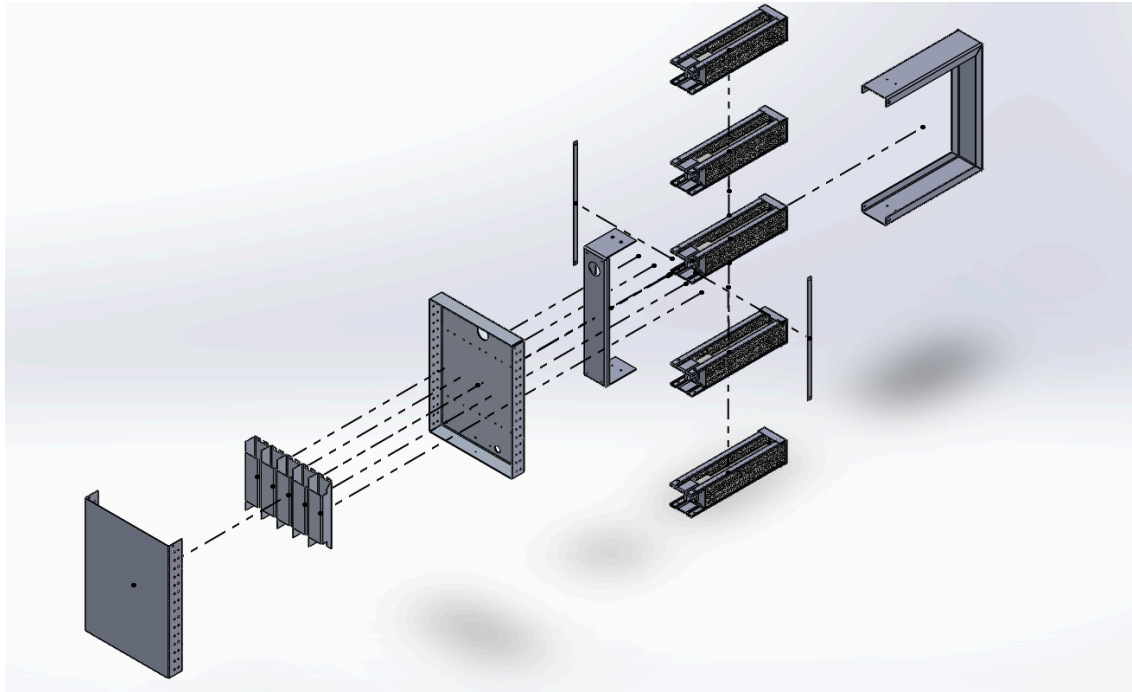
Vista explosionada del ensamblaje del Cassette de desinfección
